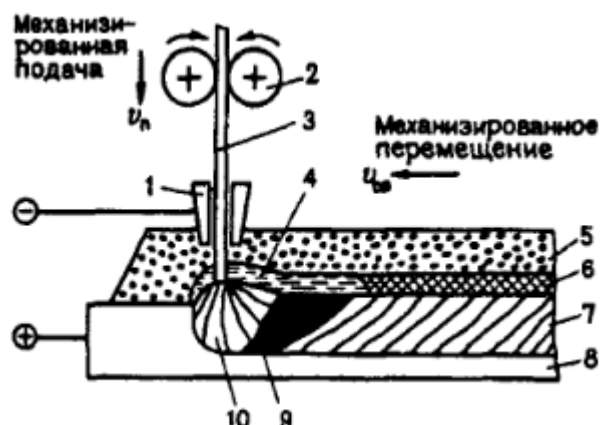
Схема автоматической сварки под флюсом
